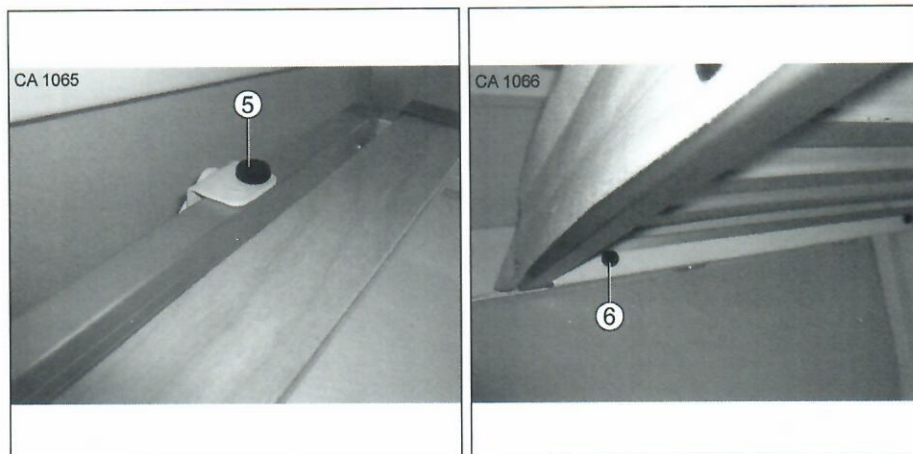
Stockbett vorn aus- und einbauen Abb. 24 Stockbett hinten aus- und einbauen
